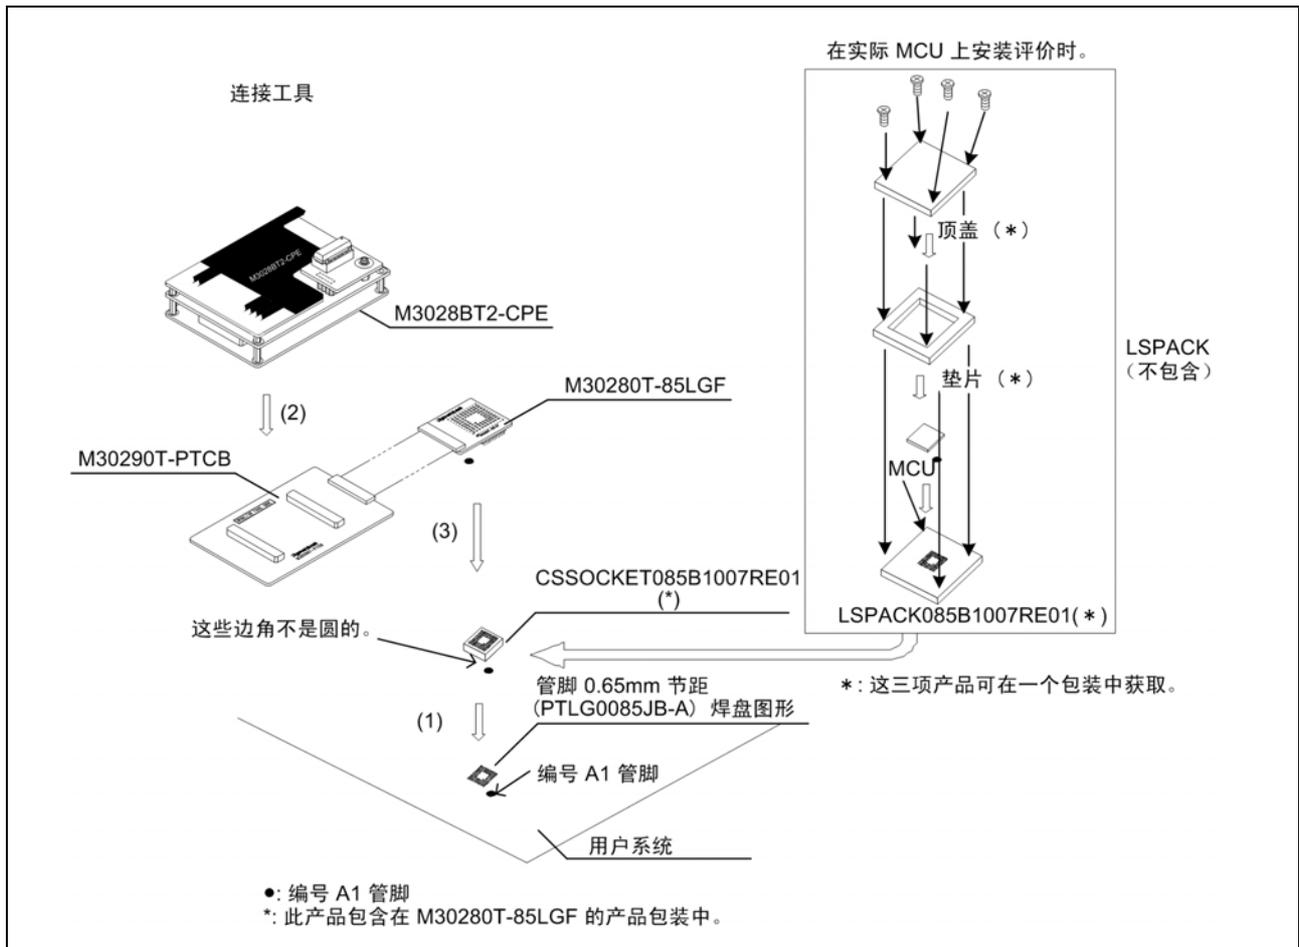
85 管脚 .65mm 节距焊盘图形的连接
